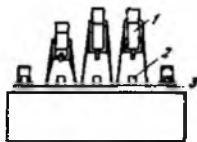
Компоновка агрегатных станков с прямолинейным перемещением заготовок
